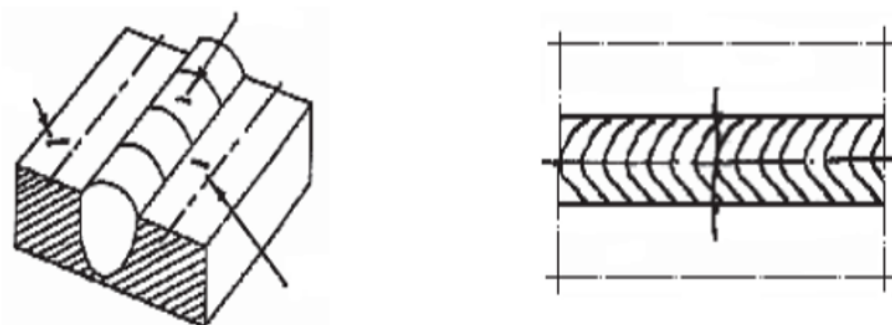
Эскиз дефекта сварного шва
